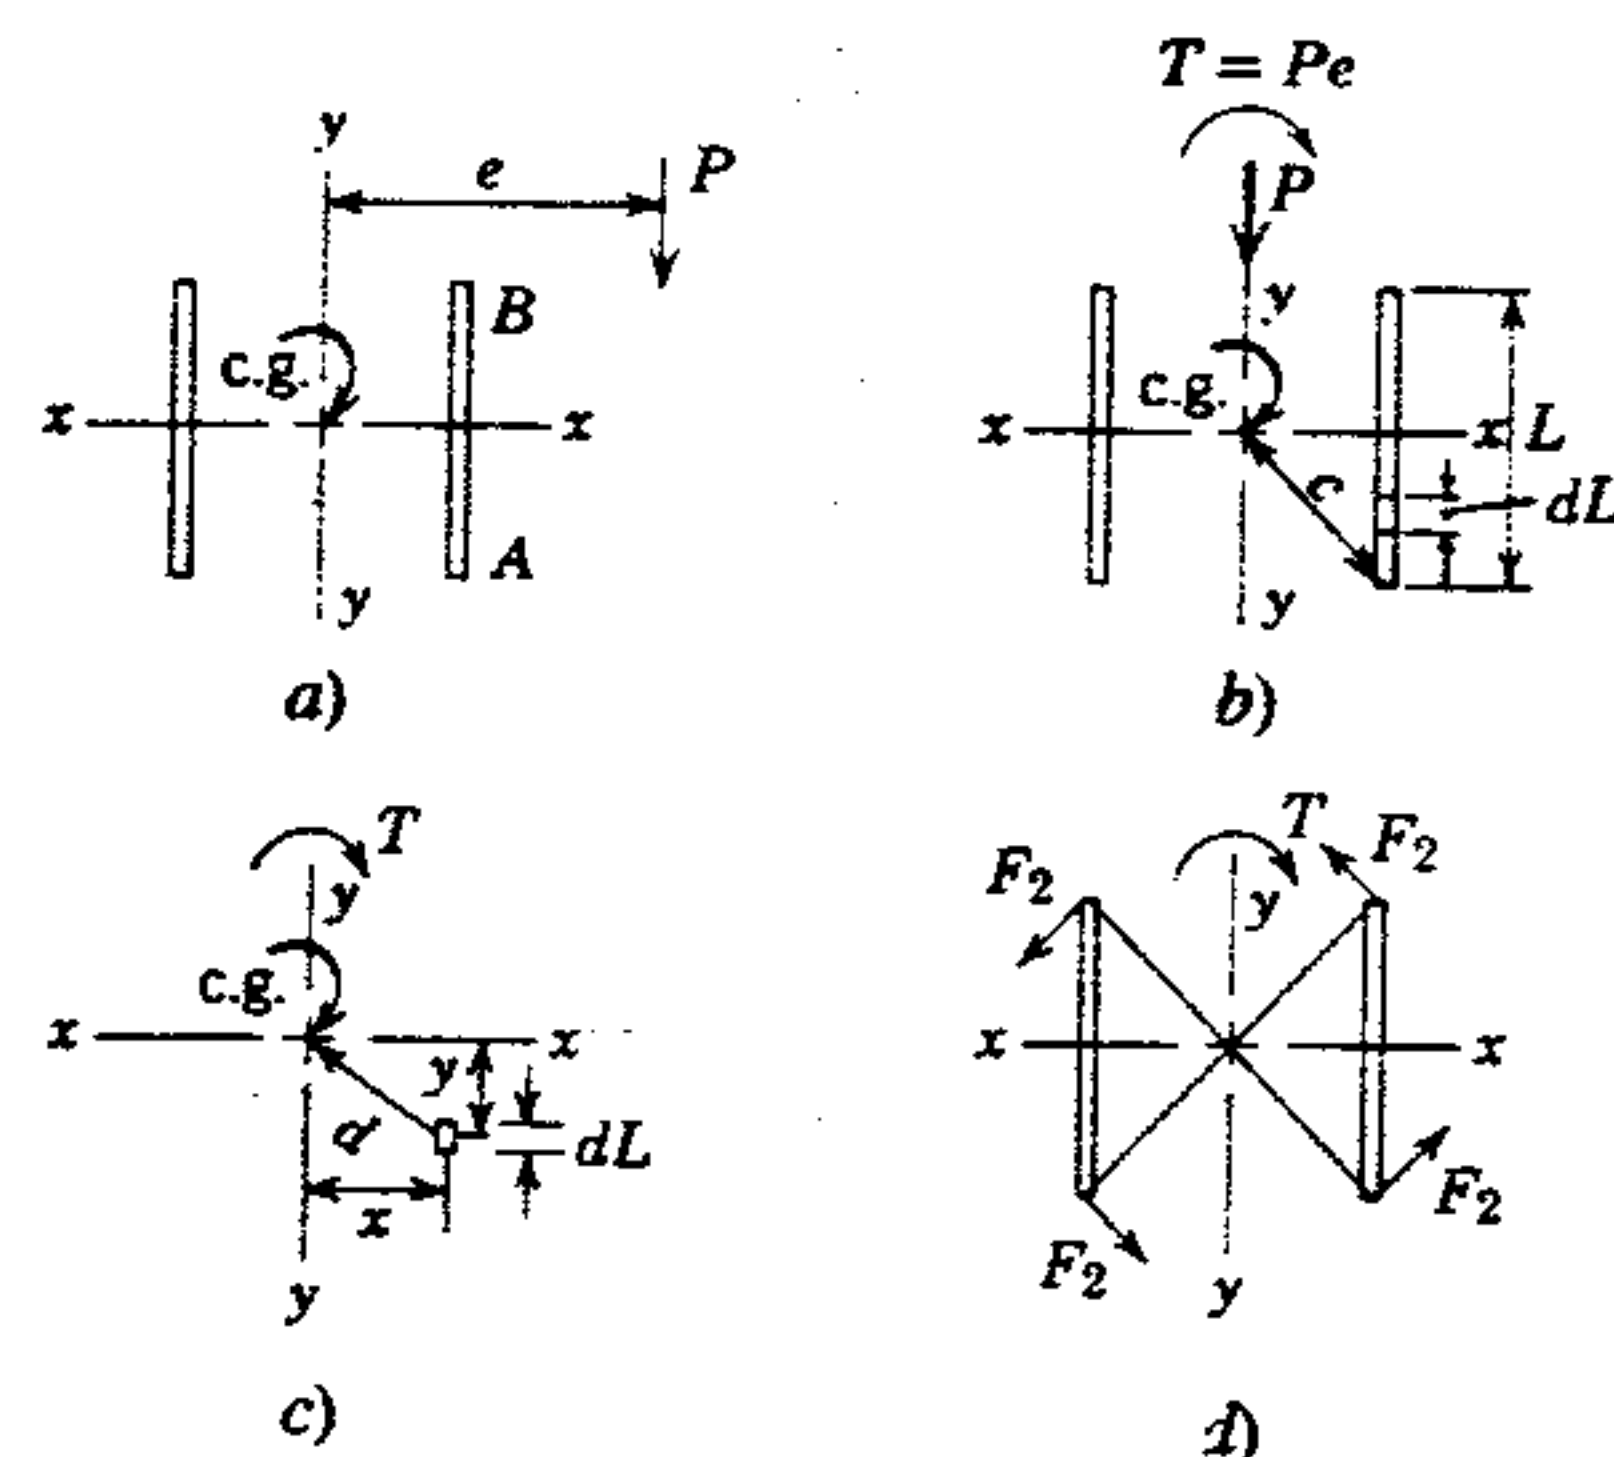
Excentricidad en el plano de soldaduras.
